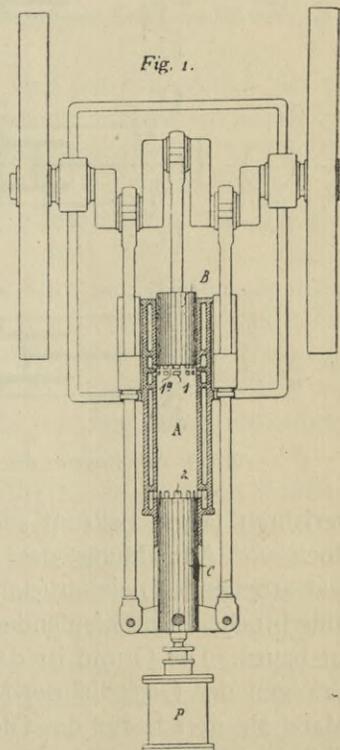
Gegenkolben-Verpuffungsmaschine von Oechelhäuser. (D. R. P. 94 111)
